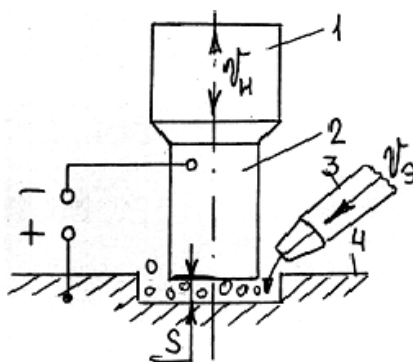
Схема поєднання ЕХО та УЗО: 1 – ультразвуковий перетворювач; 3 – сопло для подання суспензії; 2 – інструмент-електрод; 4 – заготовка
